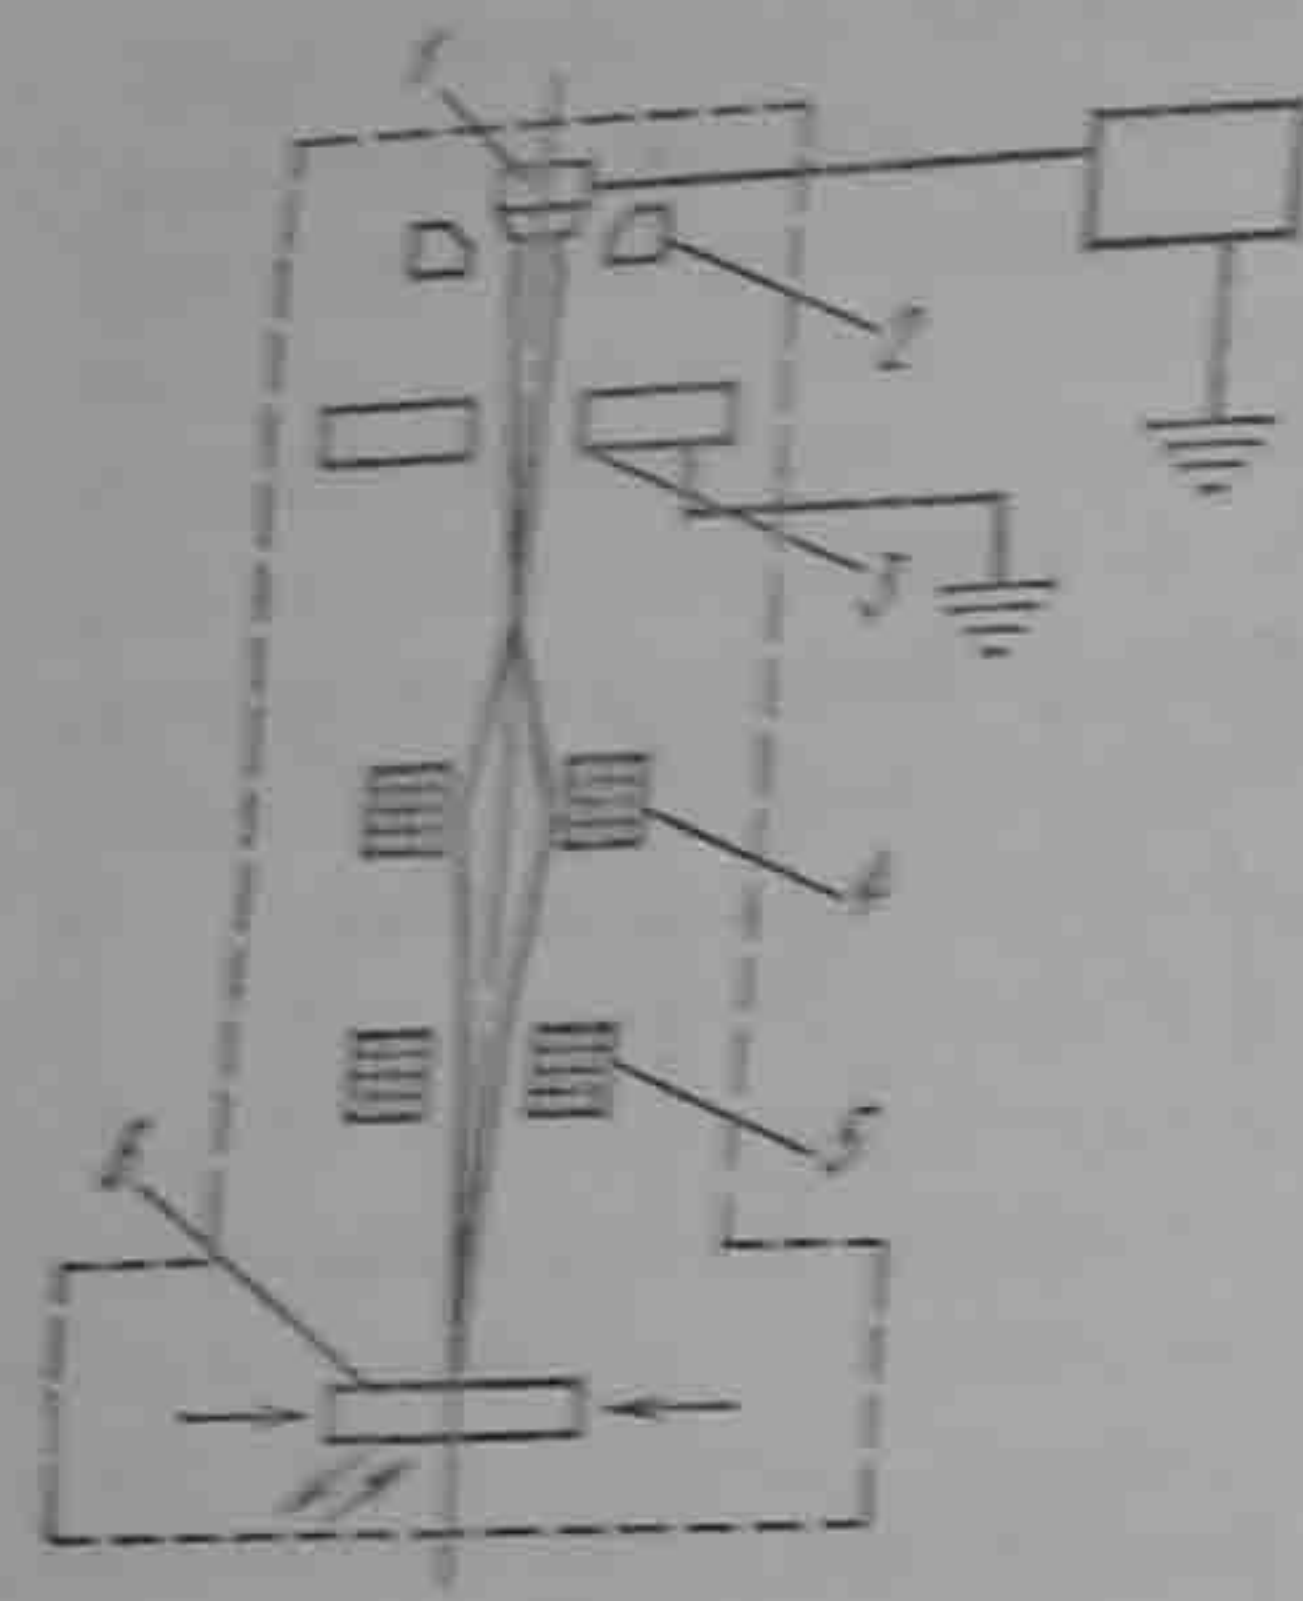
Схема установки для электронно-лучевой сварки
